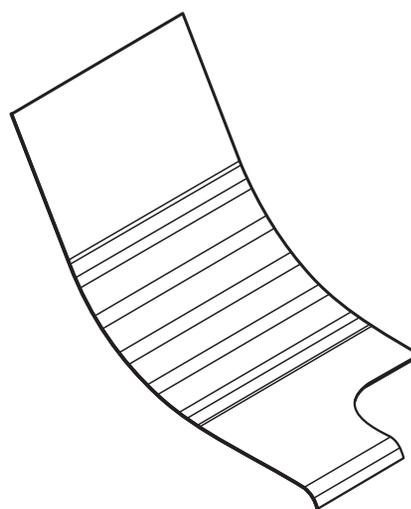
Аксонометрическое изображение деформируемой заготовки
